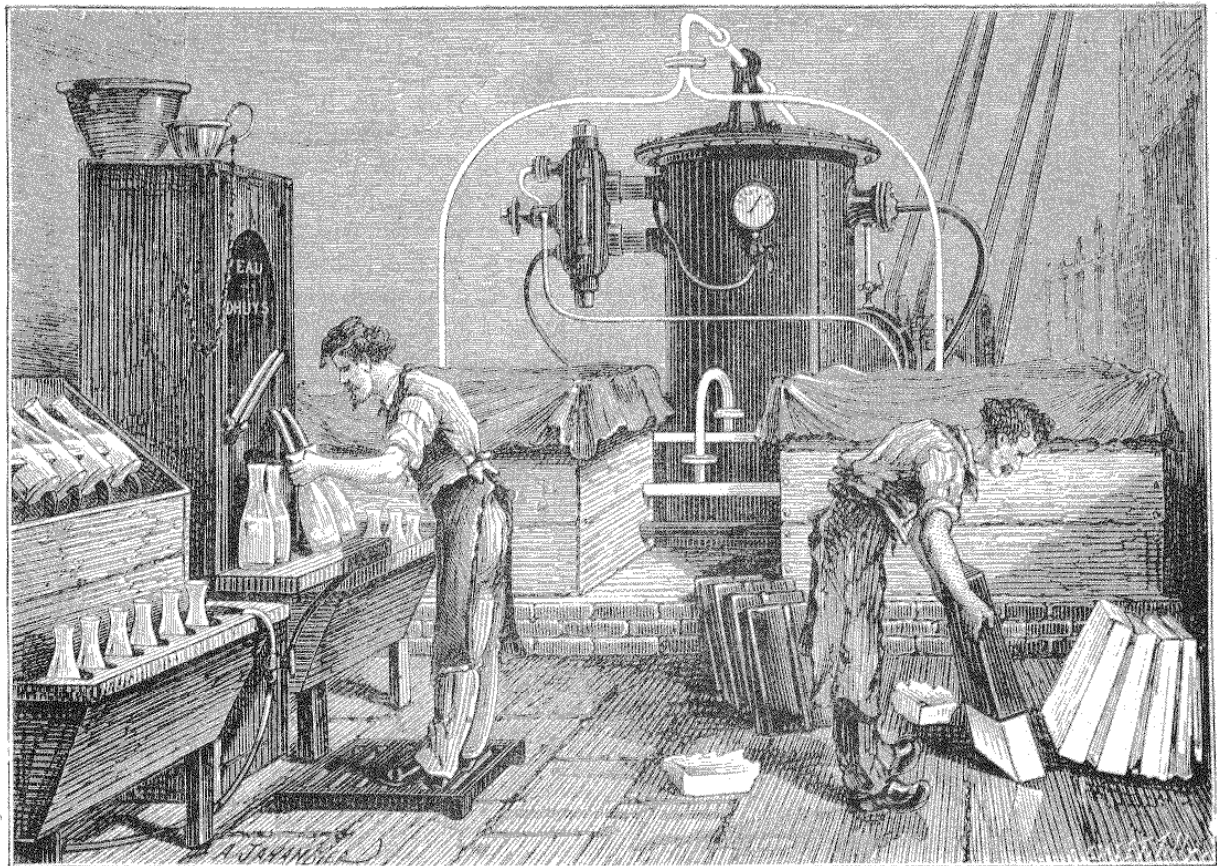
Vue d'ensemble de la machine à fabriquer la glace.
